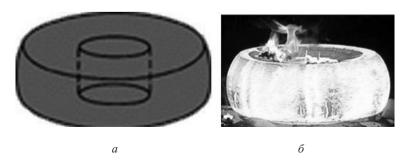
Форма заготовки кольца под кольцераскатку: a — форма заготовки; δ — нагретая заготовка
